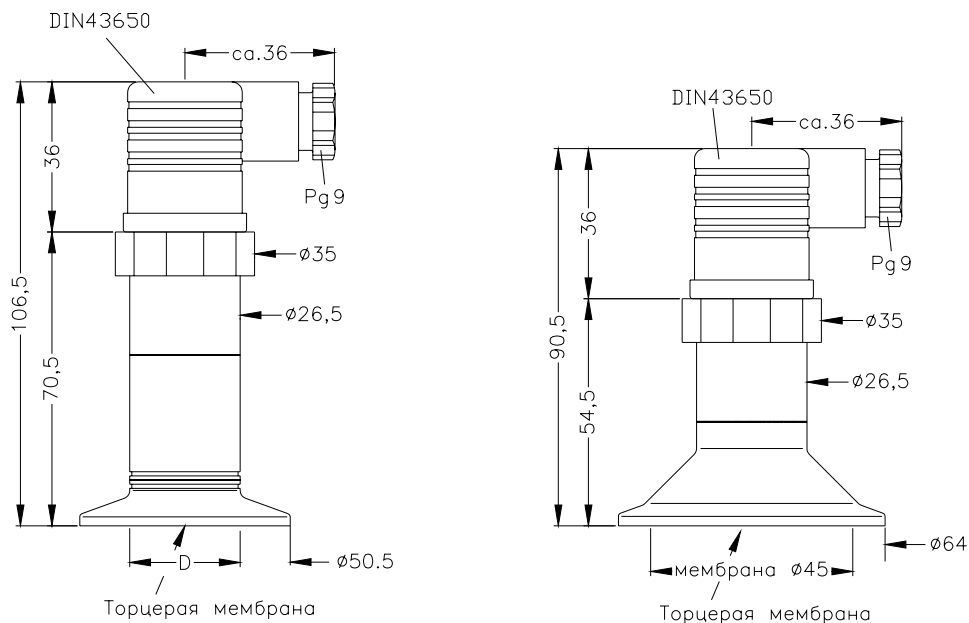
Габаритные размеры и размеры различных типов механических присоединений датчиков давления DMP 331P, DMP 331Pi
